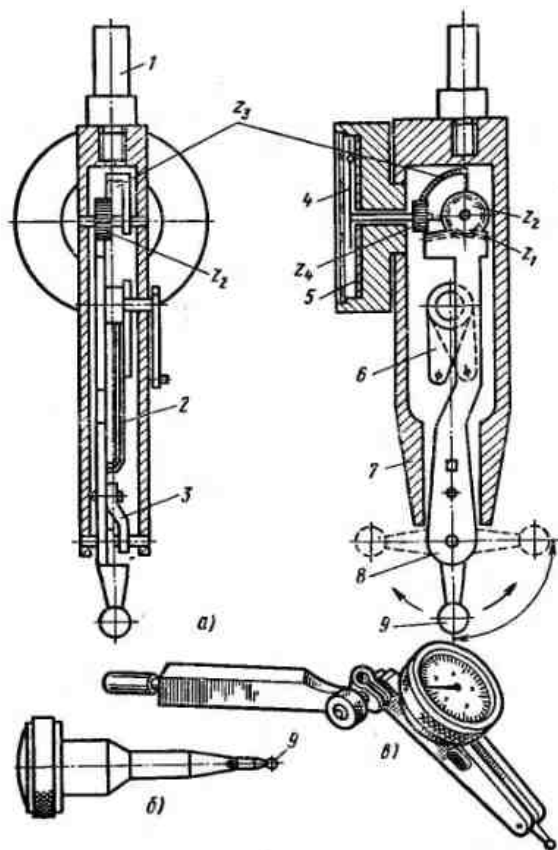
Рычажно-зубчатые измерительные головки типов ИРБ, ИРТ
